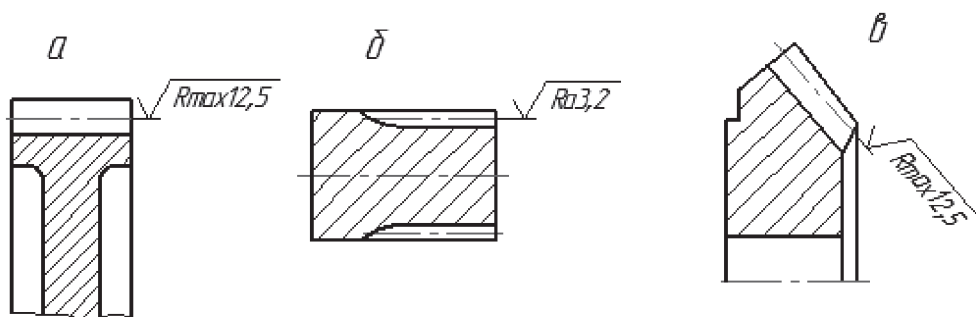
Обозначение шероховатости рабочих поверхностей зубьев зубчатых колес, шлицев
